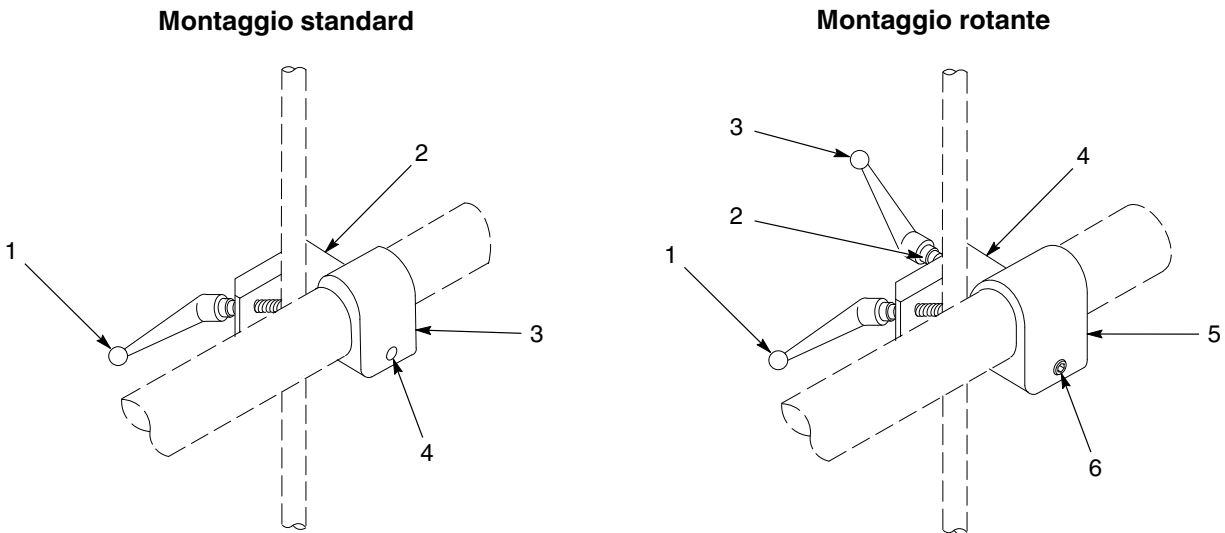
Elementi di montaggio su barra per pistole con montaggio su tubo
